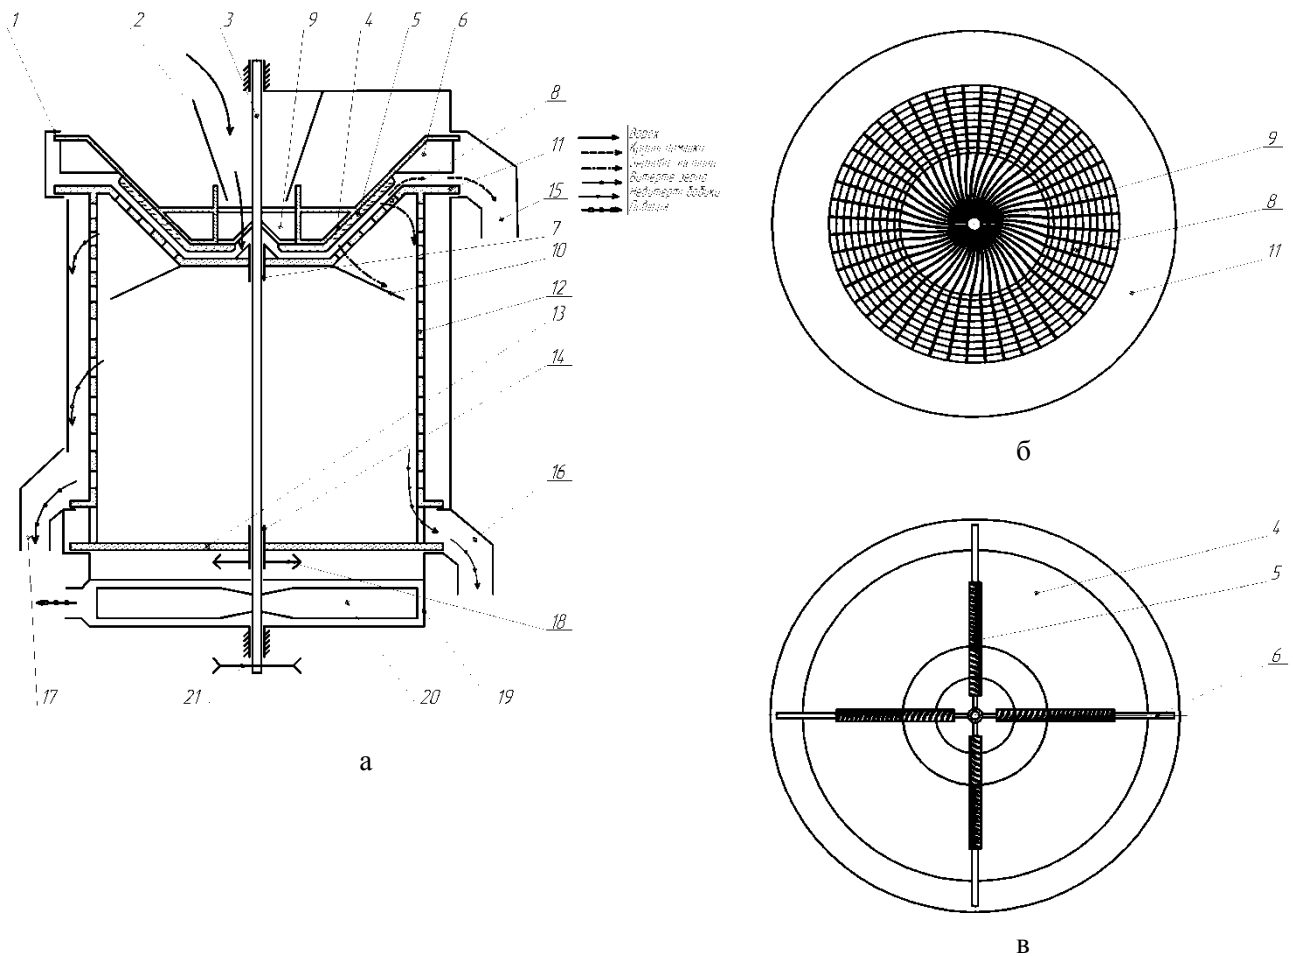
Конструктивна схема удосконаленого теркового пристрою: а – загальний вигляд; б – рухомий диска теркового пристрою; в – нерухомий диск теркового пристрою; 1 – кожух; 2 – завантажувальна воронка; 3 – вал; 4 – конічний барабан; 5 – бичі; 6 – лопатки; 7 – підшипник; 8 – дека; 9 – скребки; 10 – розсіювальний конус; 11 – кільце; 12 – циліндричне решето; 13 – диск; 14 – підшипникова опора; 15 – канал для відводу солом’яної частини вороху; 16 – канал для відводу не витертого із бобів зерна; 17 – канал для відводу очищеного насіння; 18 – автономний привід; 19 – вентилятор; 20 – лопаті; 21 – привід
